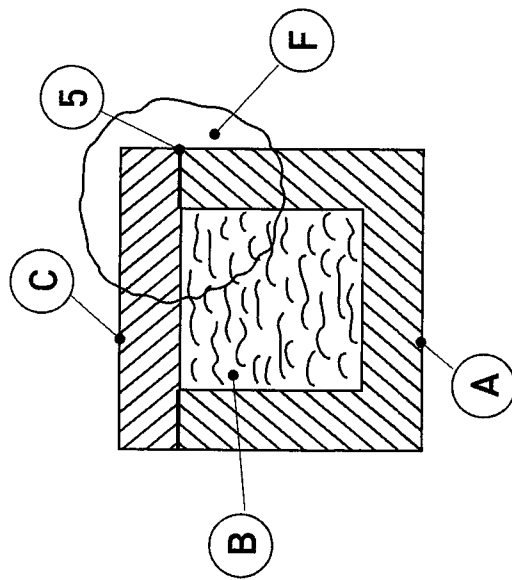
Zeigt gemäß dem Ausführungsbeispiel einen Querschnitt durch einen Stab mit dem zu einem U -Profil (U) geformten Stahlband (A) mit einer aufgeprägten Oberflächentextur (N), weiter eine Kupfereinlage (B), ein heiß aufgedrucktes Stahlband (C), mit einer Oberflächentextur (N) sowie eine Schweißverbindung (S) zwischen einem U -Profil (U) und einem Stahlband (C)
